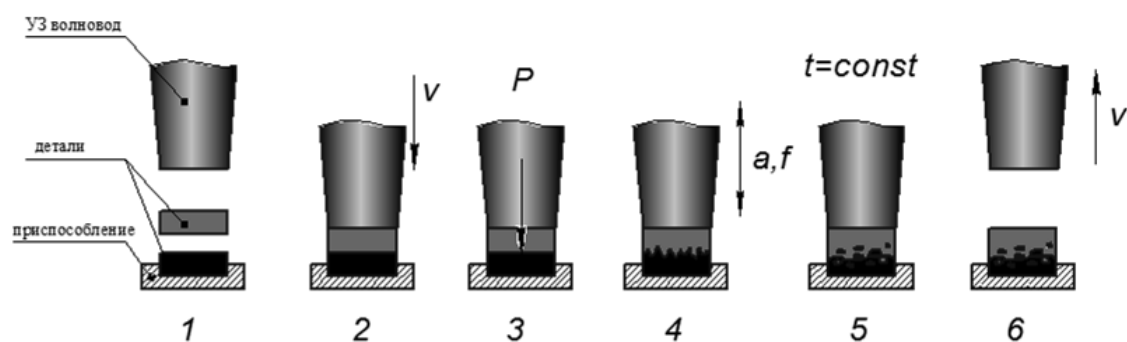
Цикл ультразвуковой сварки
